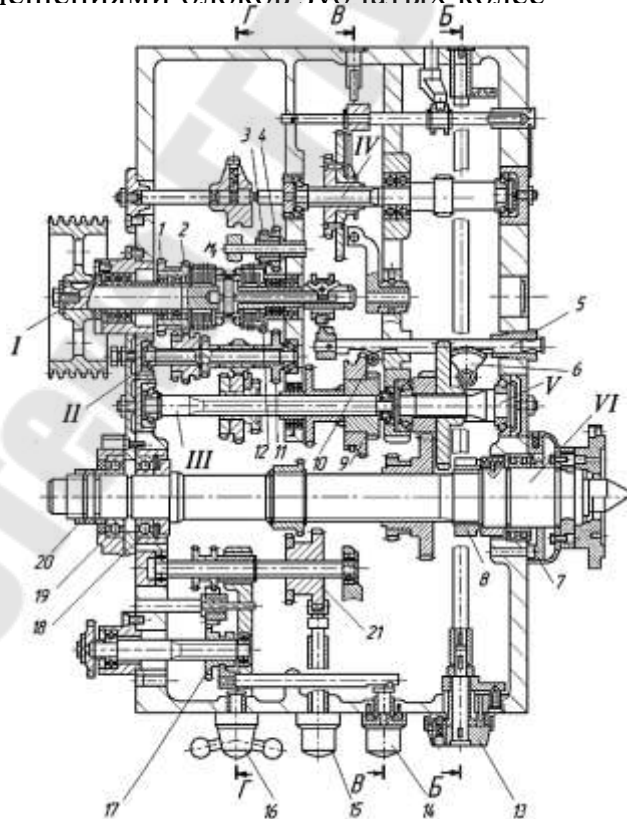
Многорукоятное управление блоками зубчатых колес коробки скоростей станка мод.16К20
